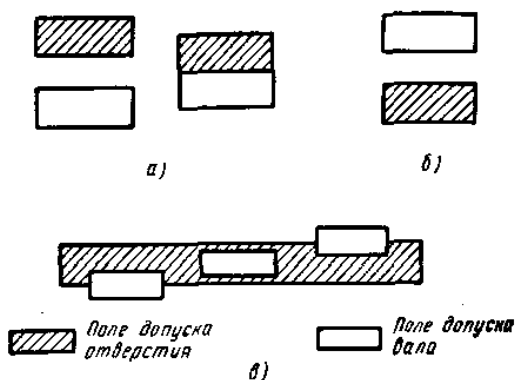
Схема расположения полей допусков отверстия и вала для различных посадок:
